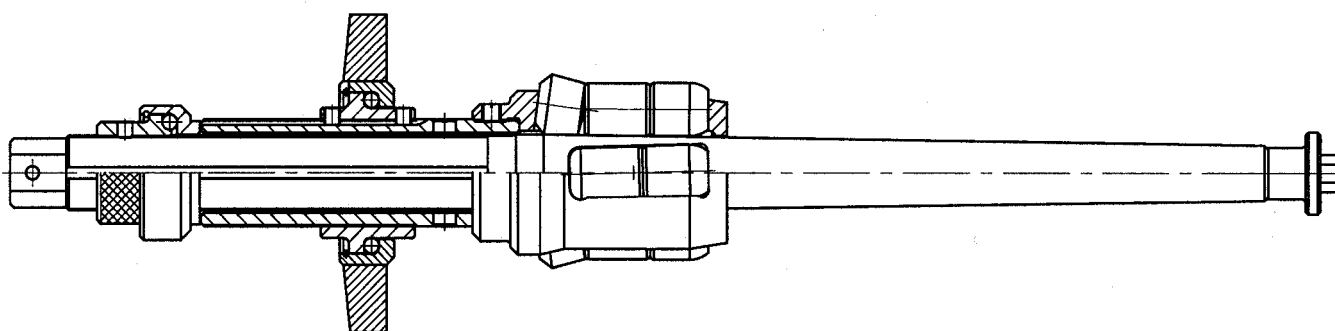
Конструкция вальцовок РО-76 и РО-102
